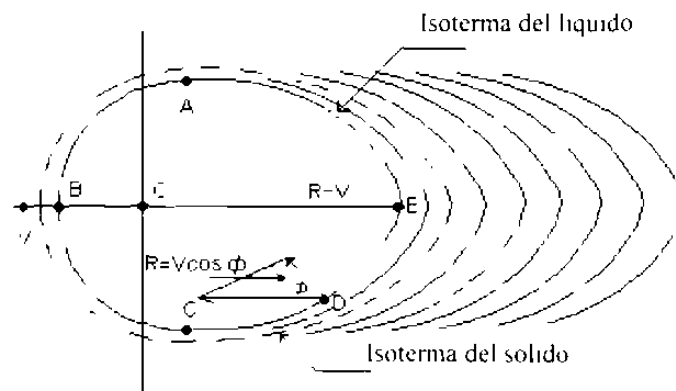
Se muestra el movimiento esquemático de una pileta líquida de soldadura
